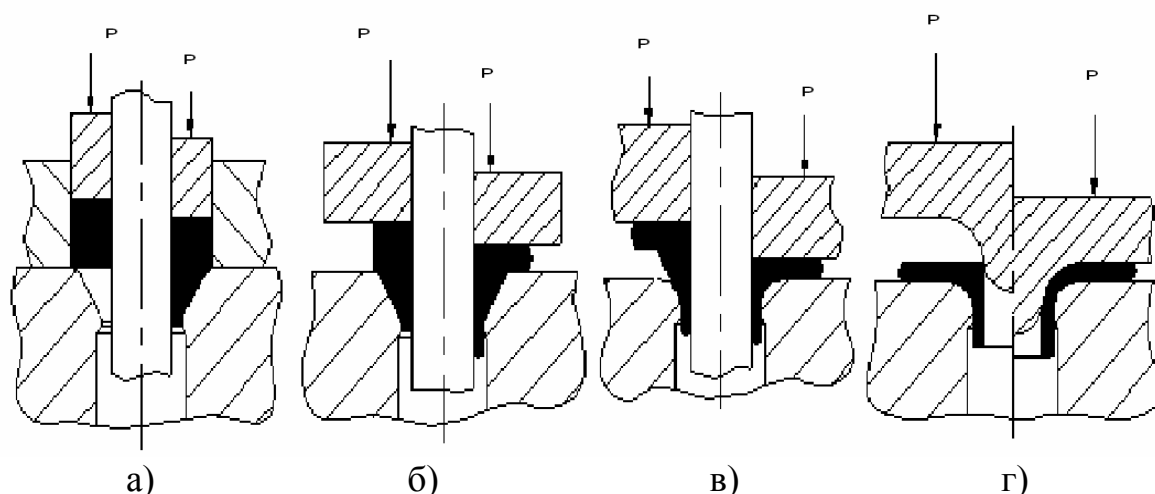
Схемы технологических операций штамповки полых заготовок с широким фланцем со сквозным отверстием из цилиндрической заготовки с отверстием: а) прямое закрытое выдавливание; б) комбинированный процесс выдавливания с высадкой; в) комбинированный процесс выдавливания с высадкой; г) калибровка.
